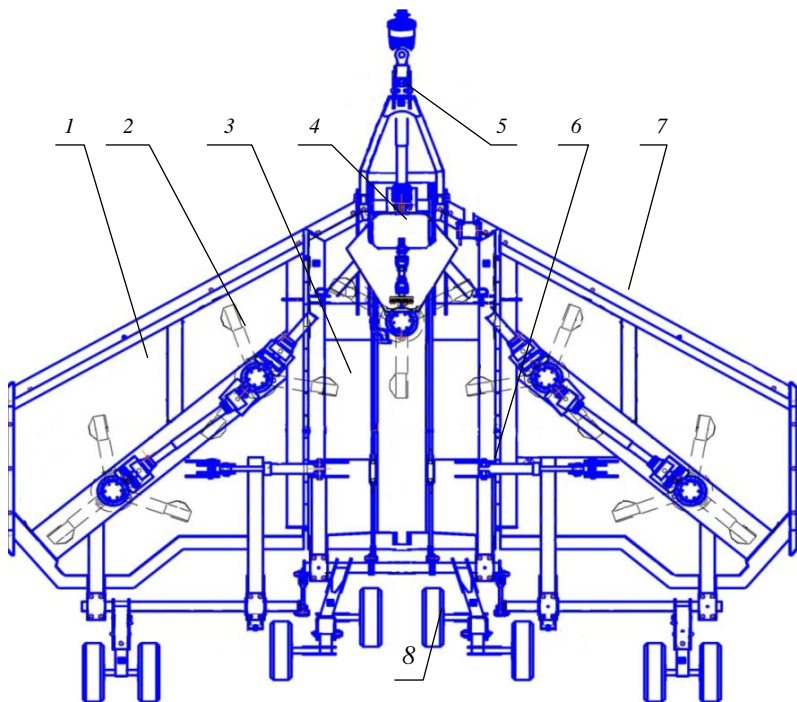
Конструктивная схема косилки КП-6,2: 1 – крыло; 2 – ротор; 3 – центральная секция; 4 – центральный редуктор; 5 – сница; 6 – гидроцилиндр гидросистемы; 7 – ограждение; 8 – колесный ход
